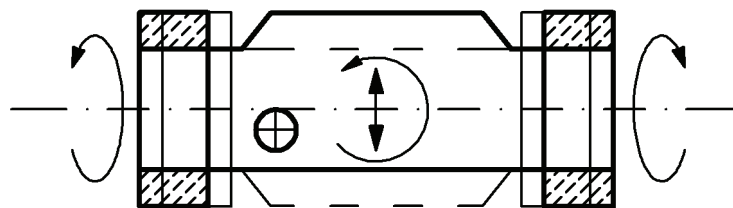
Схема способа зачистки отливок: зачистка четырех плоских поверхностей торцами абразивных кругов
